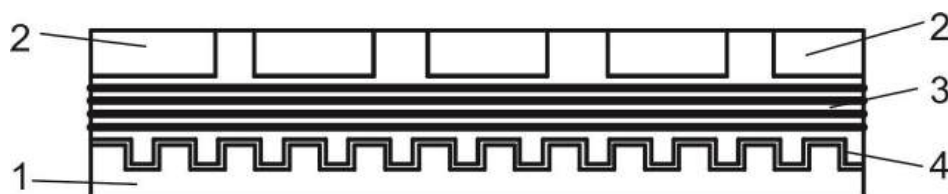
Схема приклеювання тканини до заготовки стільникового пакета: 1 – ложемент; 2 – вантаж; 3 – стільниковий пакет; 4 – стрічка
